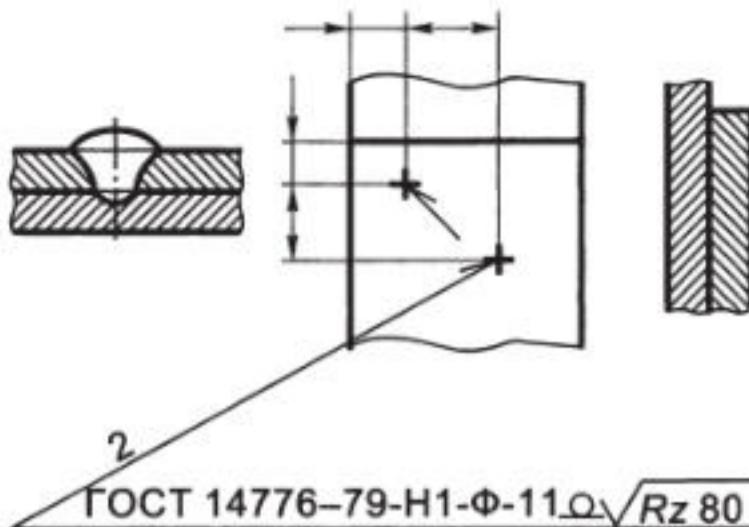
Одиночные сварные точки соединения внахлестку, выполняемые дуговой сваркой под флюсом с диаметром электрозаклепки 11 мм и снятием усиления
